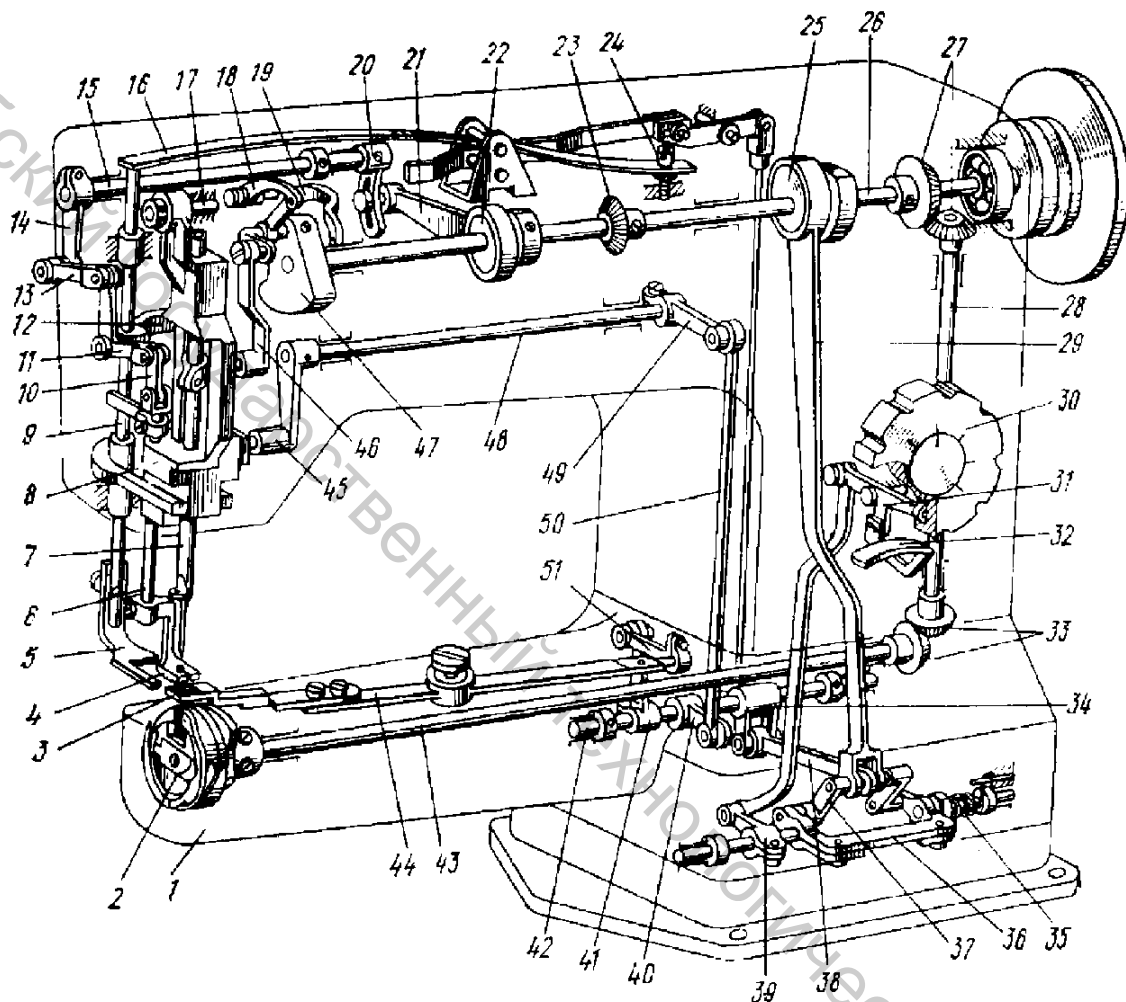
Схема одноигольной челночной швейной машины с цилиндрической платформой
